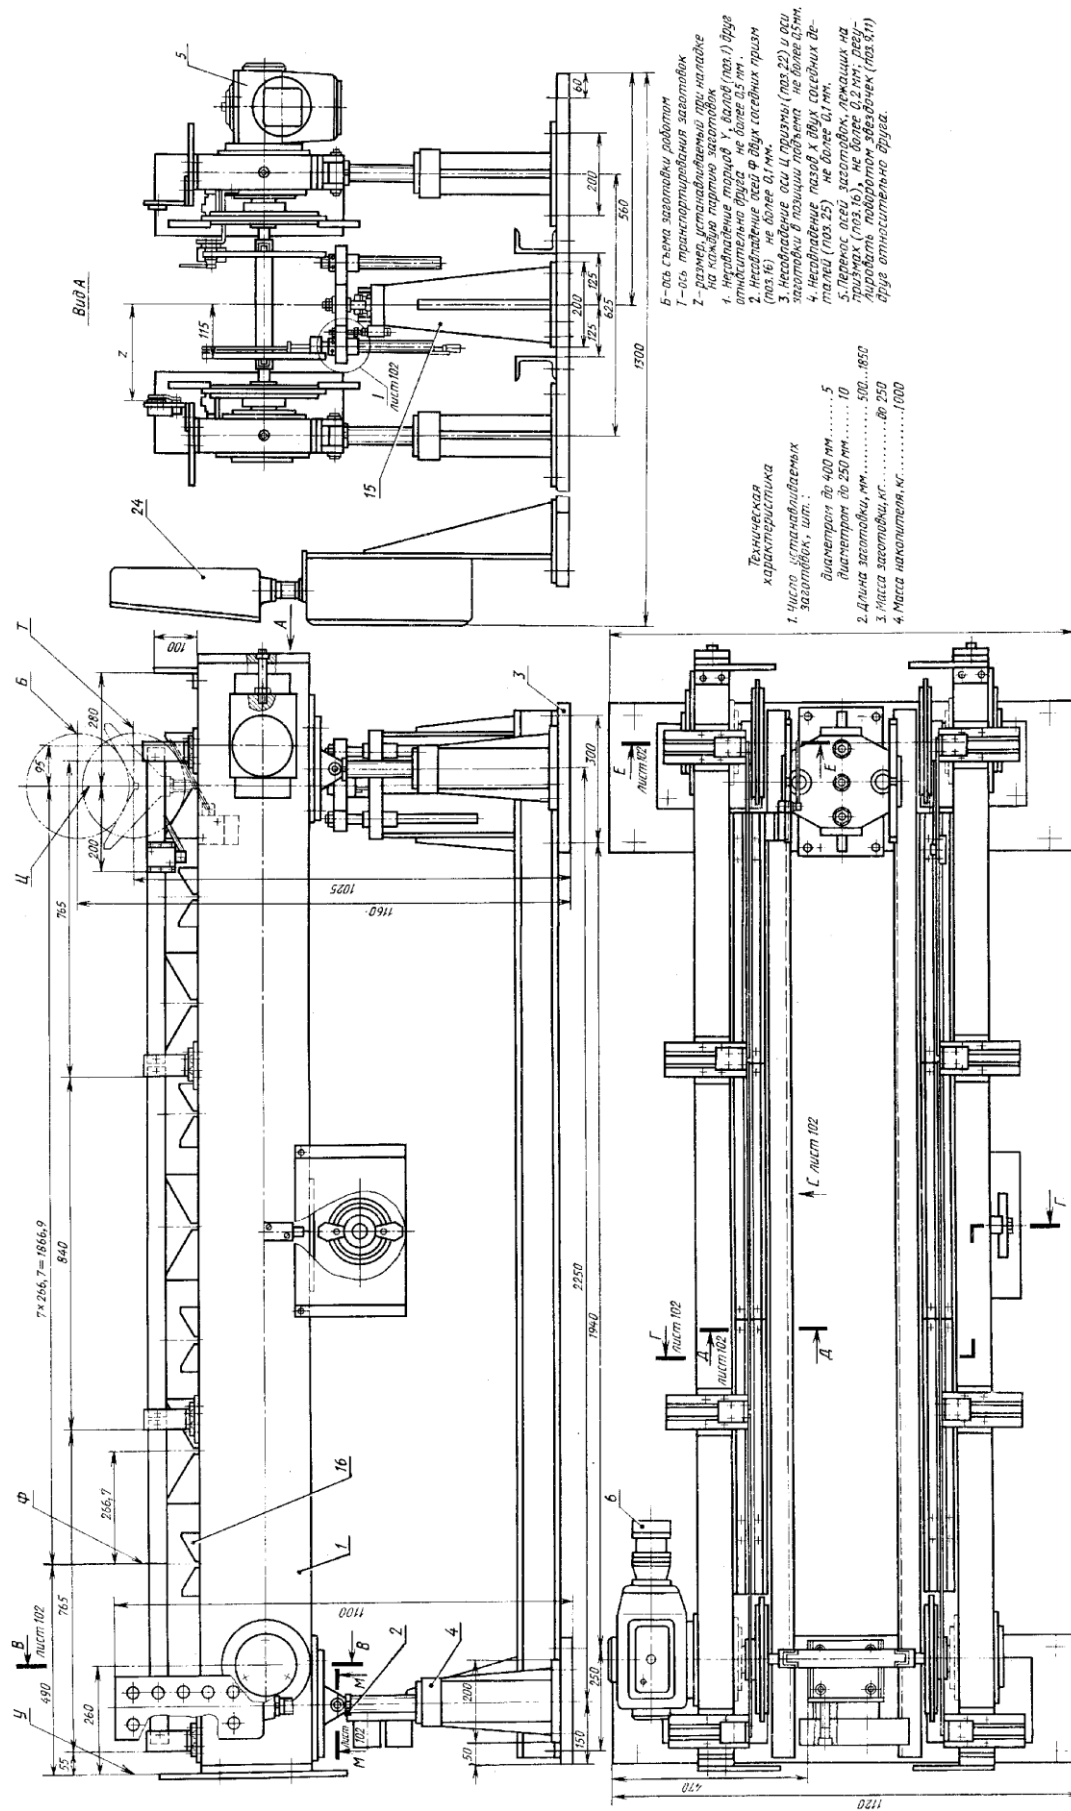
Автоматизированный накопительный пристрой для заготовок (загальний вид)
